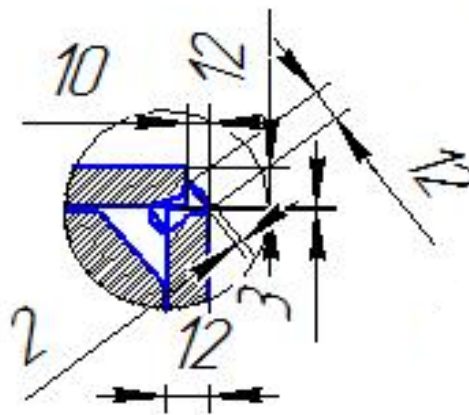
параметры сварного шва механизированной сварки У5 ГОСТ 14771-76
